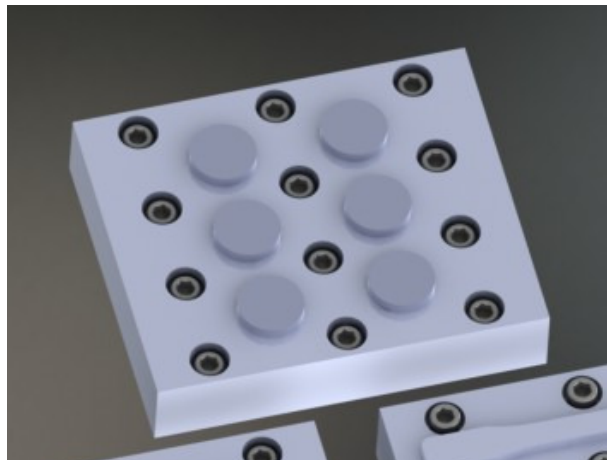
Ensamblajes de moldes para compresión (macho, hembra y base común)
